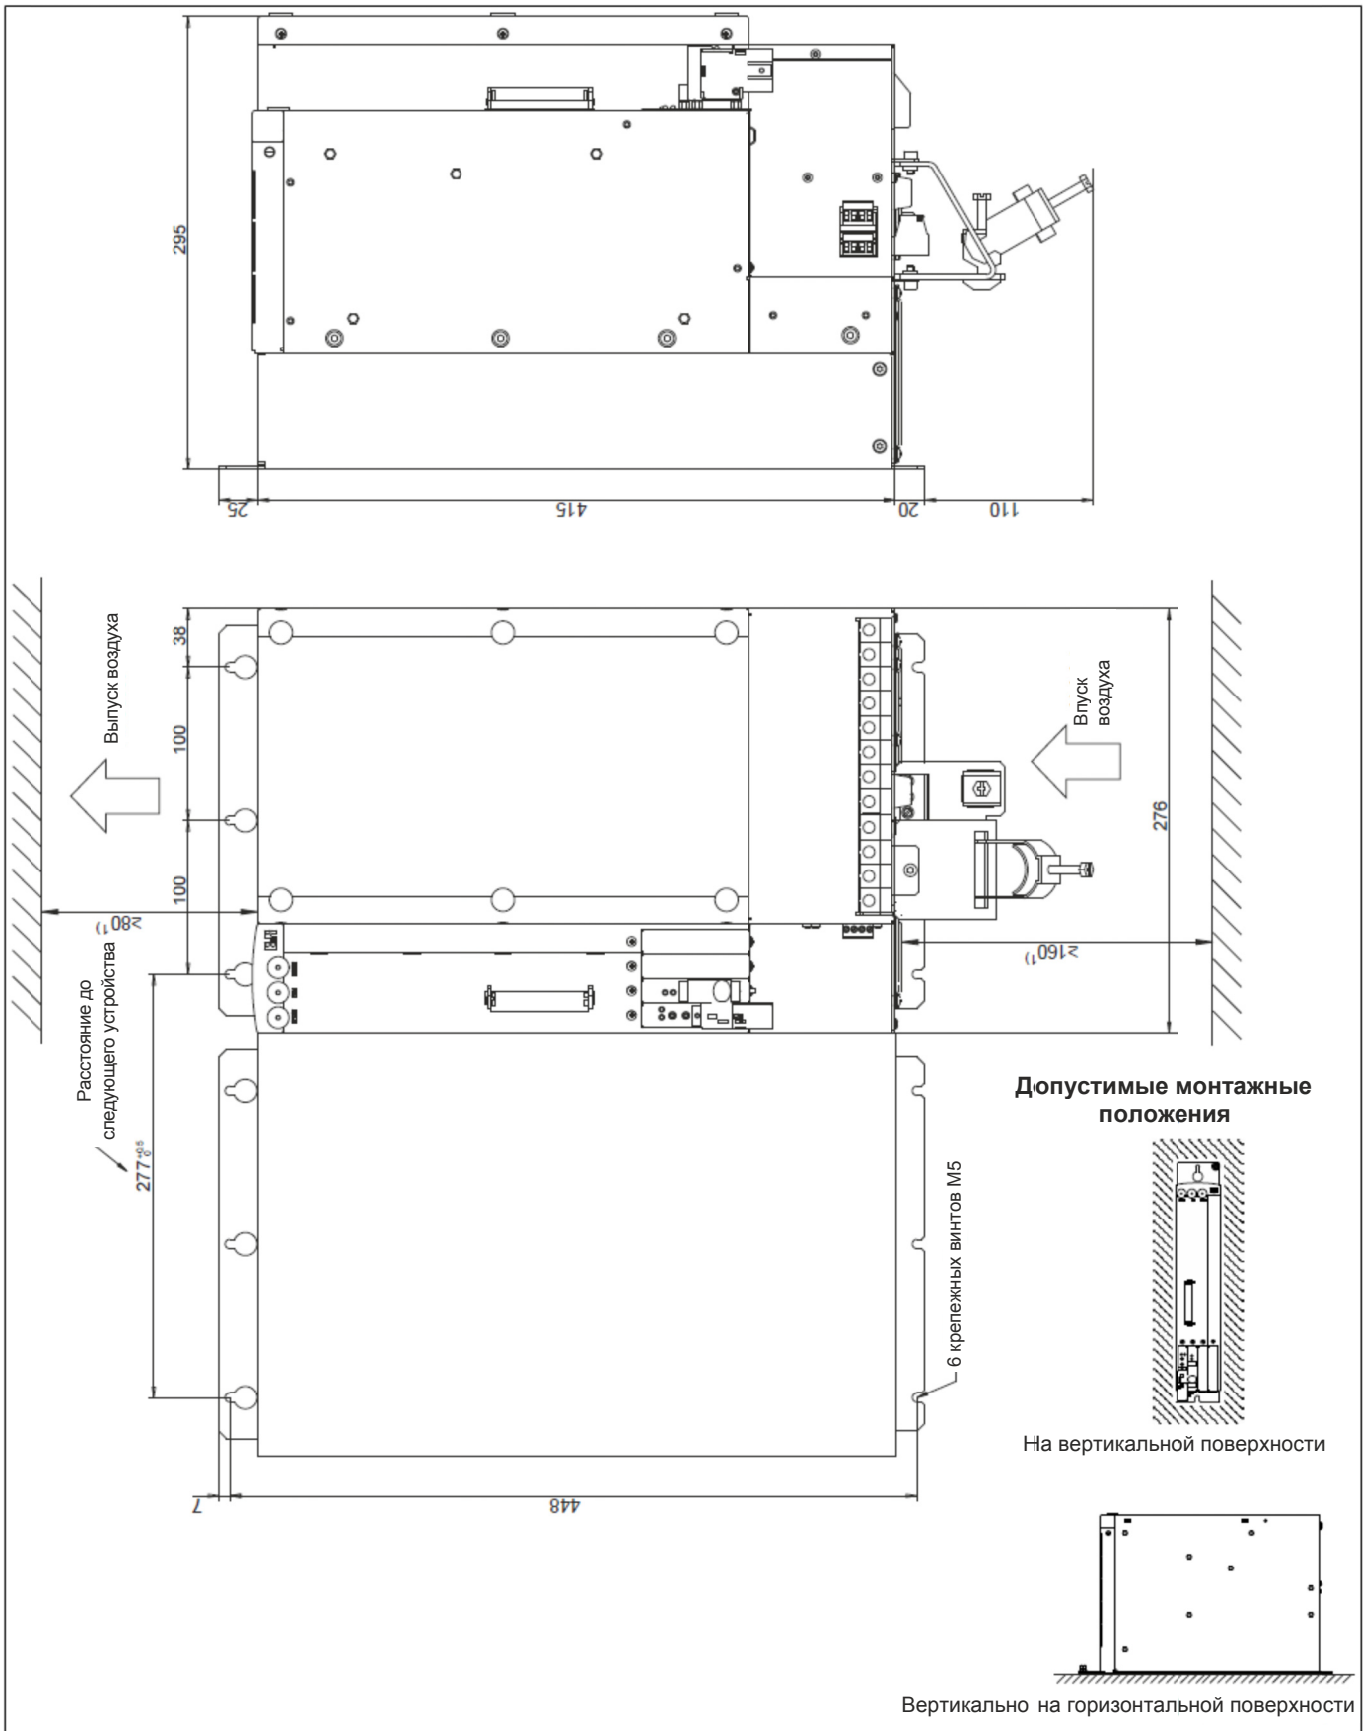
ACOPOS 1640 – Габаритный чертеж и монтажные размеры
